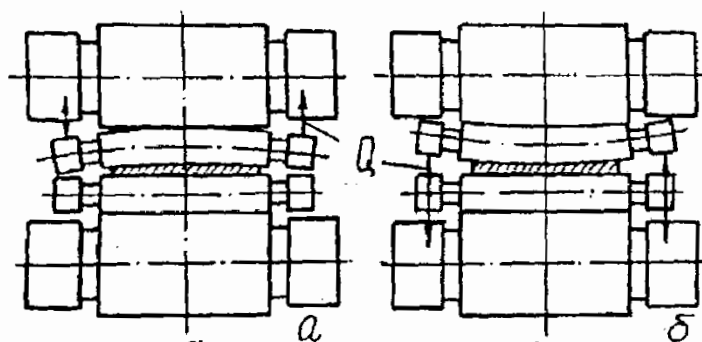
Схема гідралічного регулювання міжвалкового зозору: а - додатковий вигин; б-проти-вовигин (Q-сила проти-вигину)
